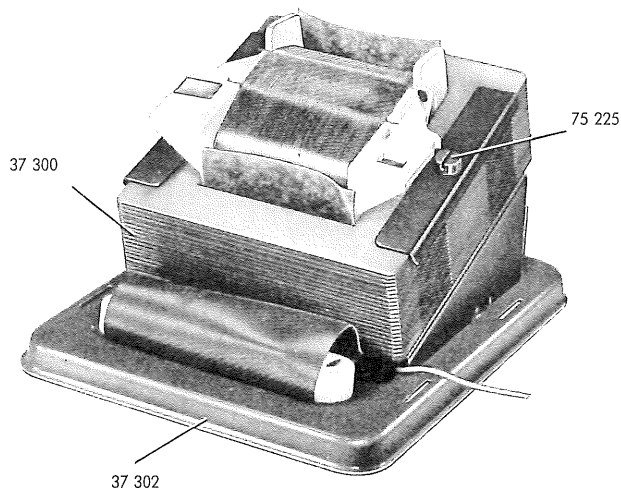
Gehäusekasten (wird in dieser Form nicht abgegeben)
